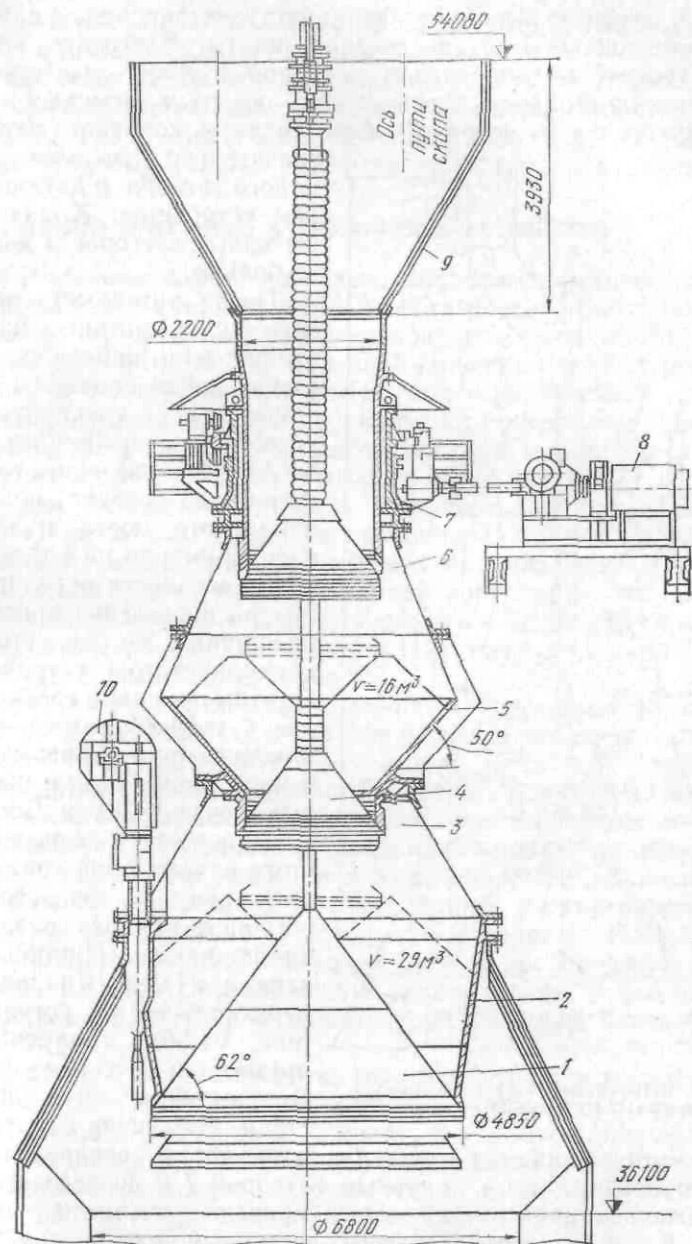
Трехконусное загрузочное устройство конструкции металлургического комбината «Запорожсталь»: 1 — большой конус; 2 — чаша; 3 — нижний газовый затвор; 4 — средний малый конус; 5 — воронка среднего конуса; 6 — верхний газовый затвор; 7 — распределитель шихты с сальниковым уплотнением вращающейся воронки; 8 — привод вращения распределителя шихты; 9 — приемная воронка; 10 — измеритель уровня шихты
